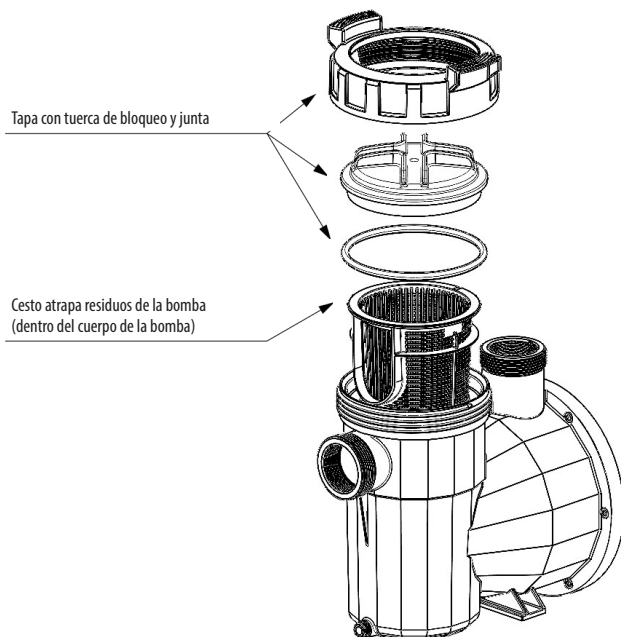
PLANO DE DESPIECE CONJUNTO CUERPO BOMBA
